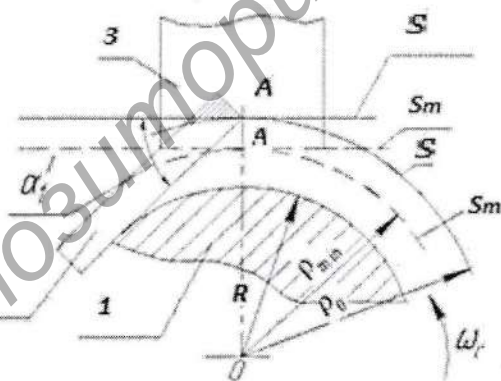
Схема переднего торца несущего цилиндра с заготовкой:
